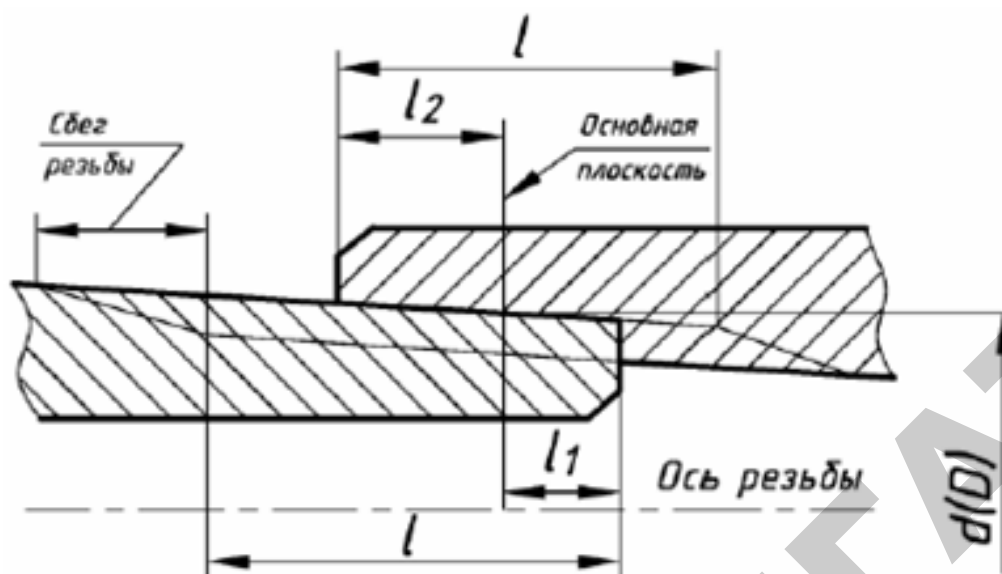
Профиль и основные параметры трубной конической резьбы
